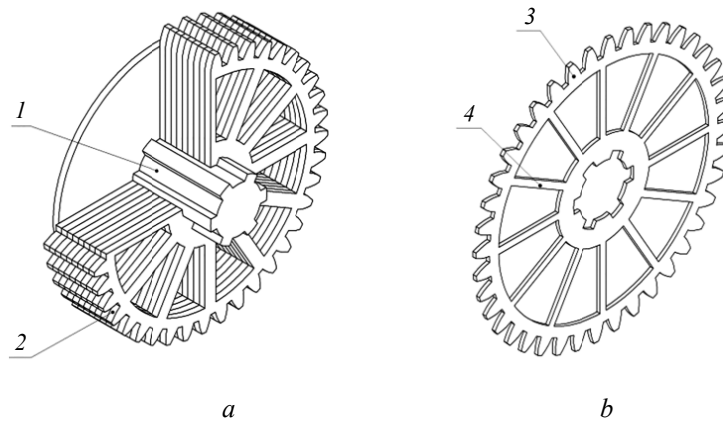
Составное колесо со спицами (RU 221909 U1): *a* – колесо в сборе; *b* – зубчатый диск
